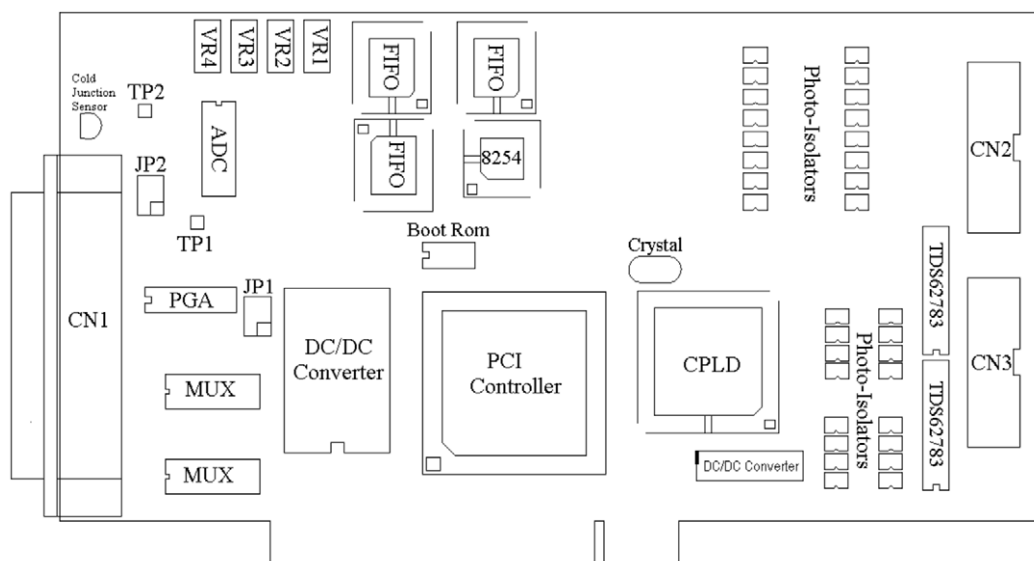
PCI-9114DG 采集卡 PCB 设计图
